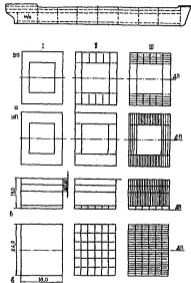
К вопросу о выборе системы набора перекрытий: а - перекрытие палубы; б - бортовое перекрытие; в - декинское перекрытие; I - общий контур перекрытия; II - расположение основных поперечных связей; III - расположение связей главного направления
